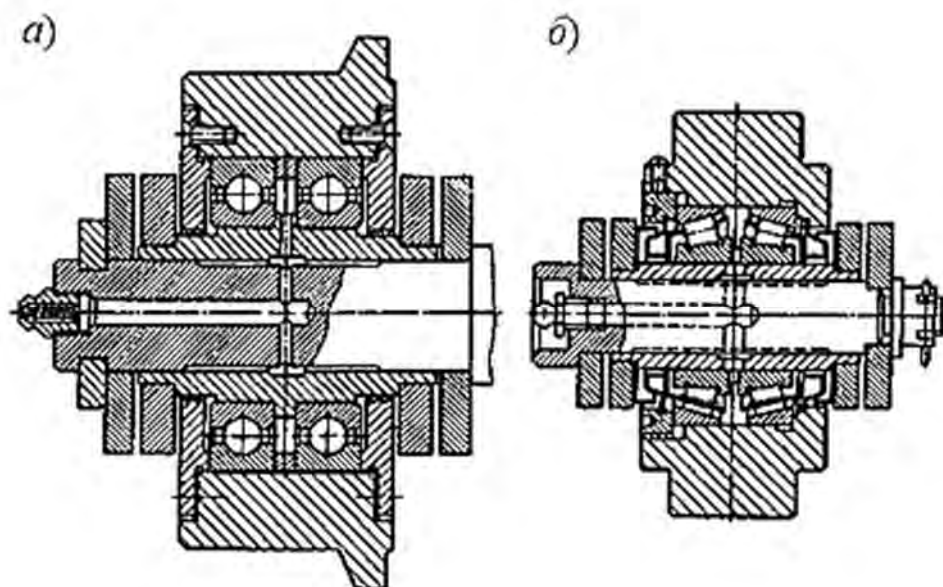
Узлы катковой цепи на подшипниках качения: *а* – с ребрами на катках; *б* – с гладкими катками
